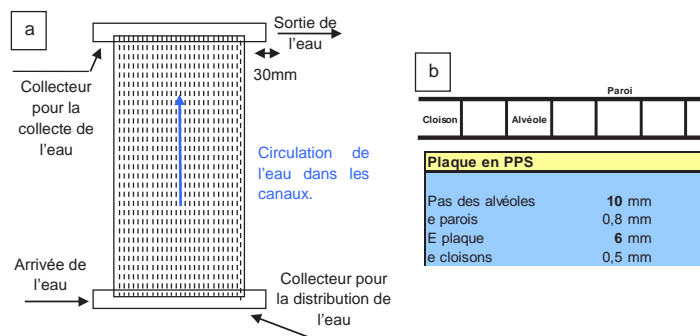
Design et dimensionnement de l'absorbeur solaire. vue générale (a) et vue en coupe avec dimensions (b)
